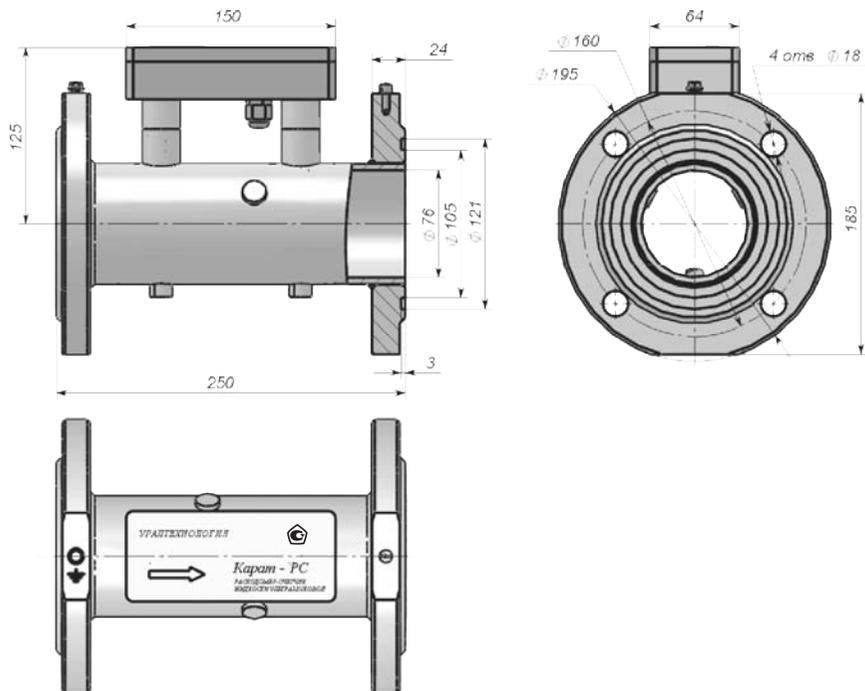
Габаритные и установочные размеры расходомера КАРАТ-РС-80
